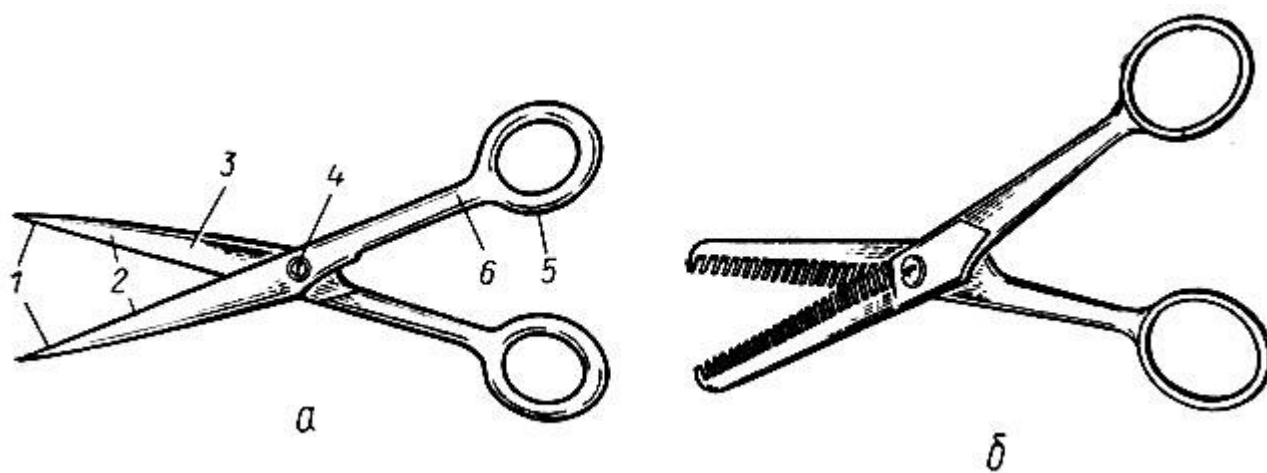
Ножницы парикмахерские: а - прямые; б - зубчатые; 1 - концы; 2 - жало; 3 - рабочие поверхности; 4 - скрепляющий винт; 5 - кольцо; 6 - рычаг
